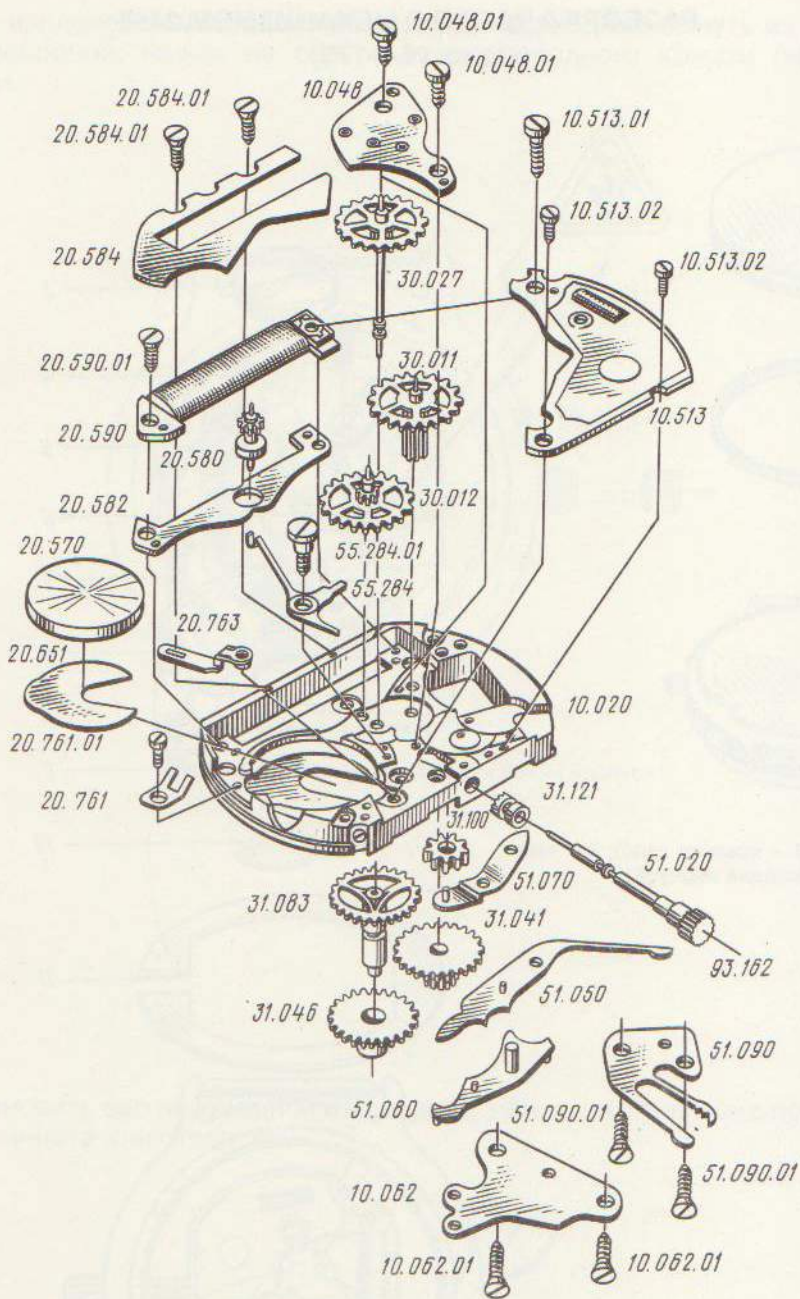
Детали и сборочные единицы механизма часов 2456:
